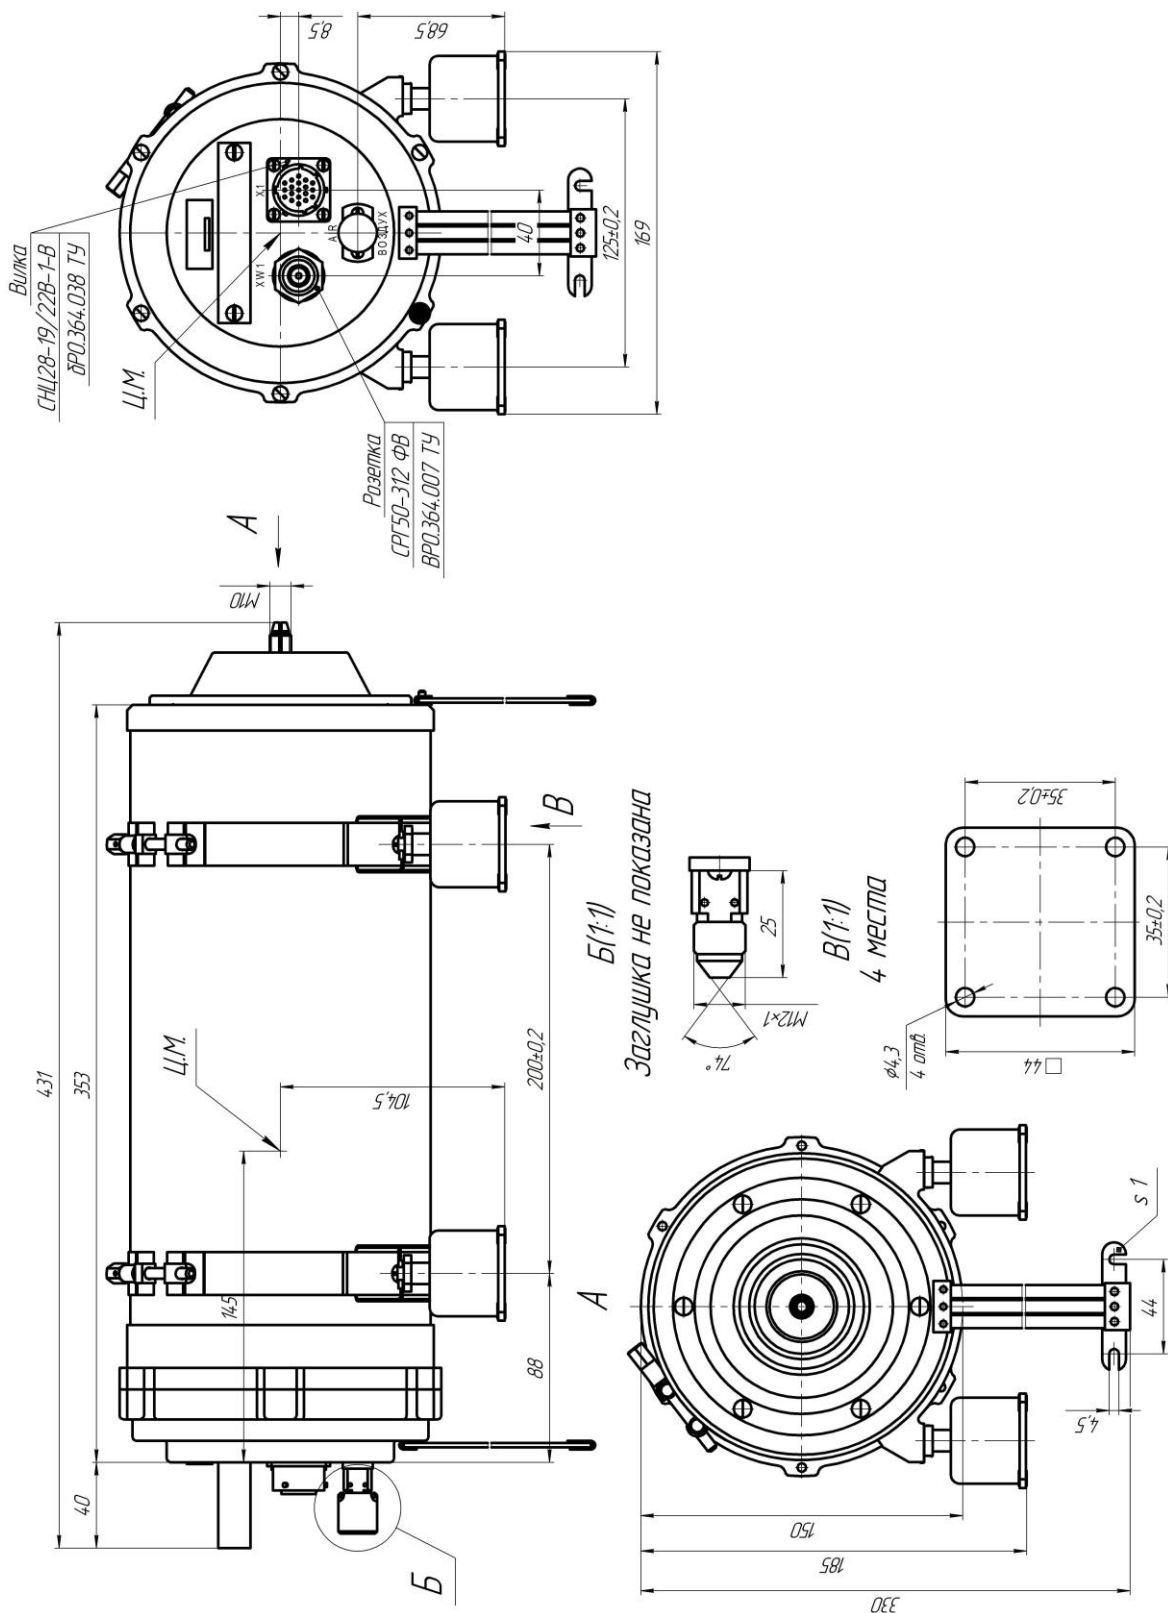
Габаритный чертеж блока Б5А2-ПрП
